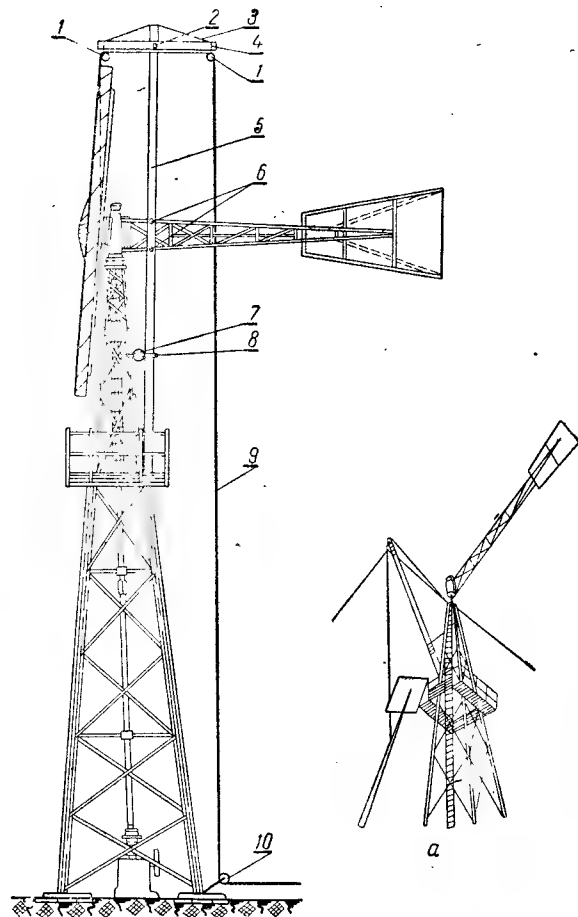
Оснастка для снятия ветроколеса и бокового плана двигателя ТВ-8:
